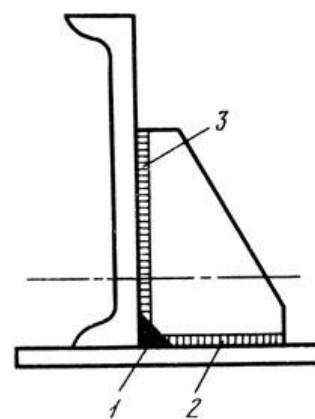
Правильная последовательность сварки узла:
